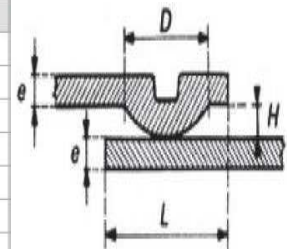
Soudage par bossages : exemples typiques [4].
